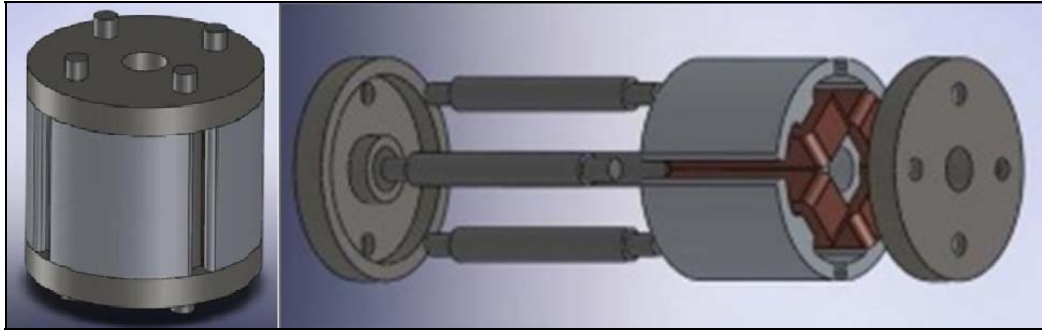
a Gruppo pistone, assemblato – Fig. 1b Gruppo pistone esploso
